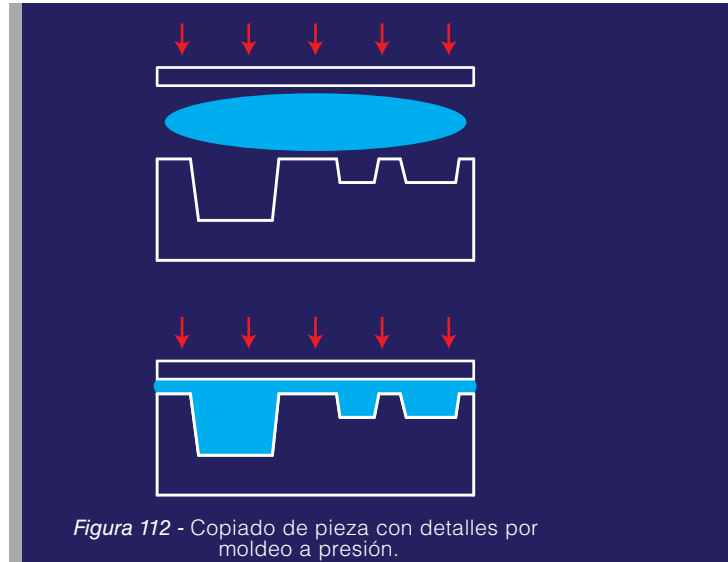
Copiado de pieza con detalles por moldeado a presión.
